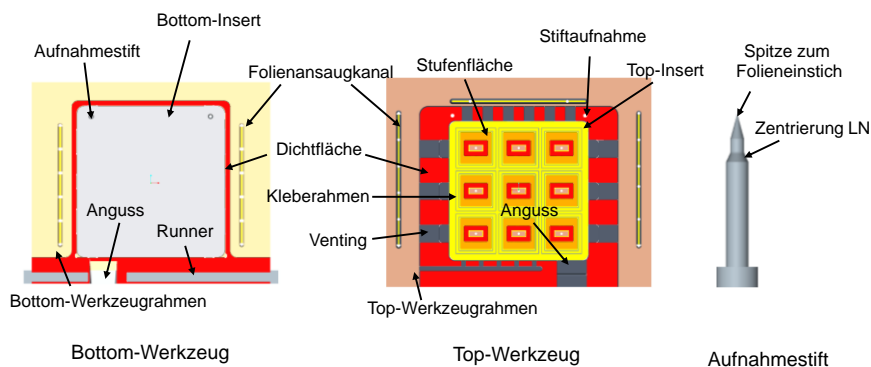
CAD-Darstellung des zusammengebauten Bottom- und Top-Werkzeugeinsatzes.
